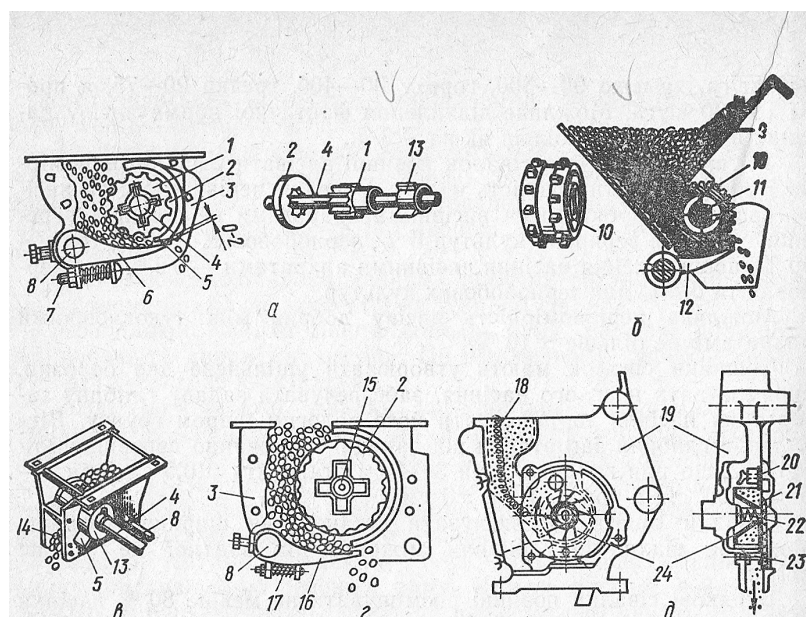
Висівні апарати котушкового типу: а, б – рядкових сівалок; в – трав'яних сівалок; г, д – овочевих сівалок; 1, 10 і 24 – котушки; 2 – розетка; 3 і 19 – корпуси; 4, 11 і 15 – вали; 5 – ребро муфти; 6, 12, 16 – клапани; 7 – регулювальний болт; 8 – вісь; 9 – заслінка; 13 – муфта; 14 – нерухоме дно; 17 і 22 – пружини; 18 – ворушилка; 20 – диск; 21 – вікно; 23 – болт
